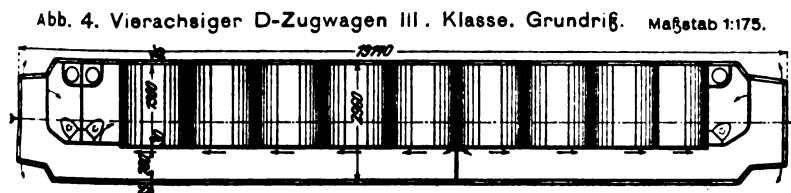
Vierachsiger D-Zugwagen III. Klasse. Grundriß. Maßstab 1:175.
